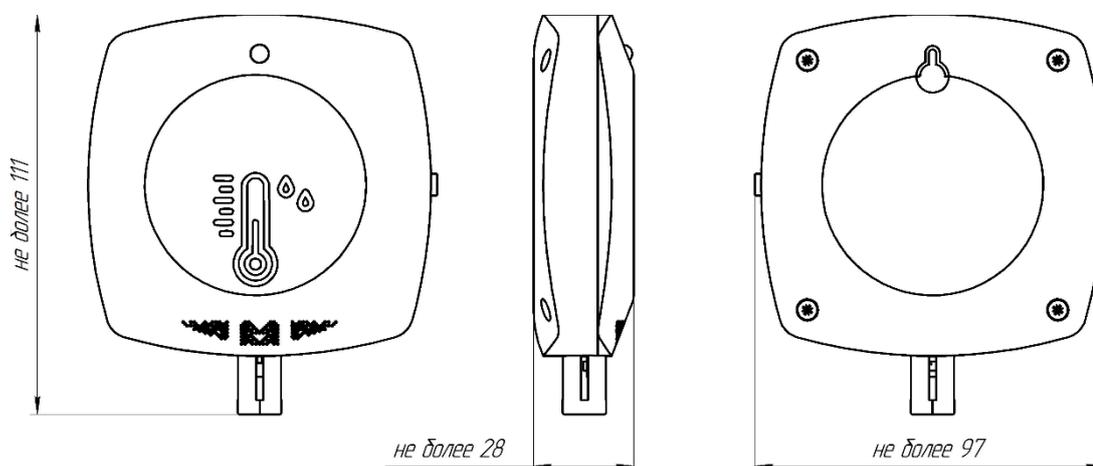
габаритные размеры ПИ-002/11 М.Д
